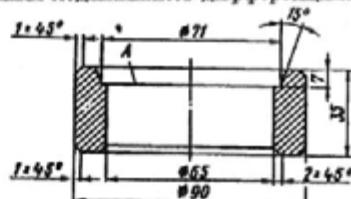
Подставка под картер редуктора при выпрессовывании наружного кольца переднего подшипника:
